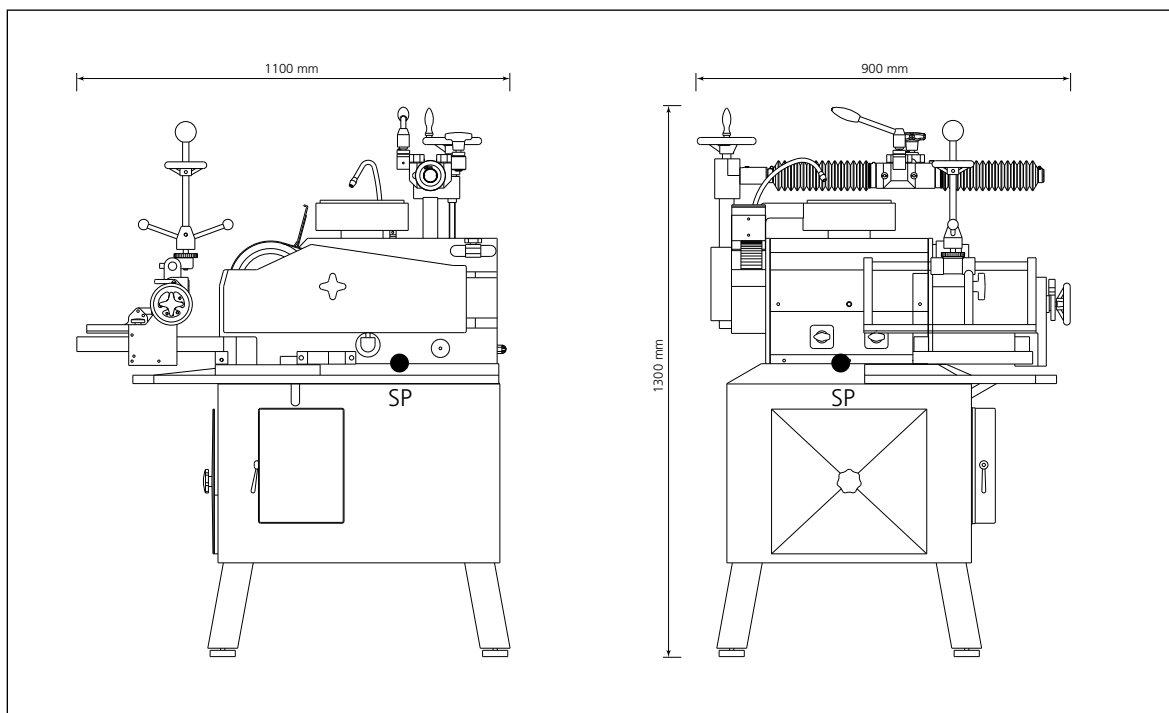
Dimensions en mm (version sur socle S200 S)
